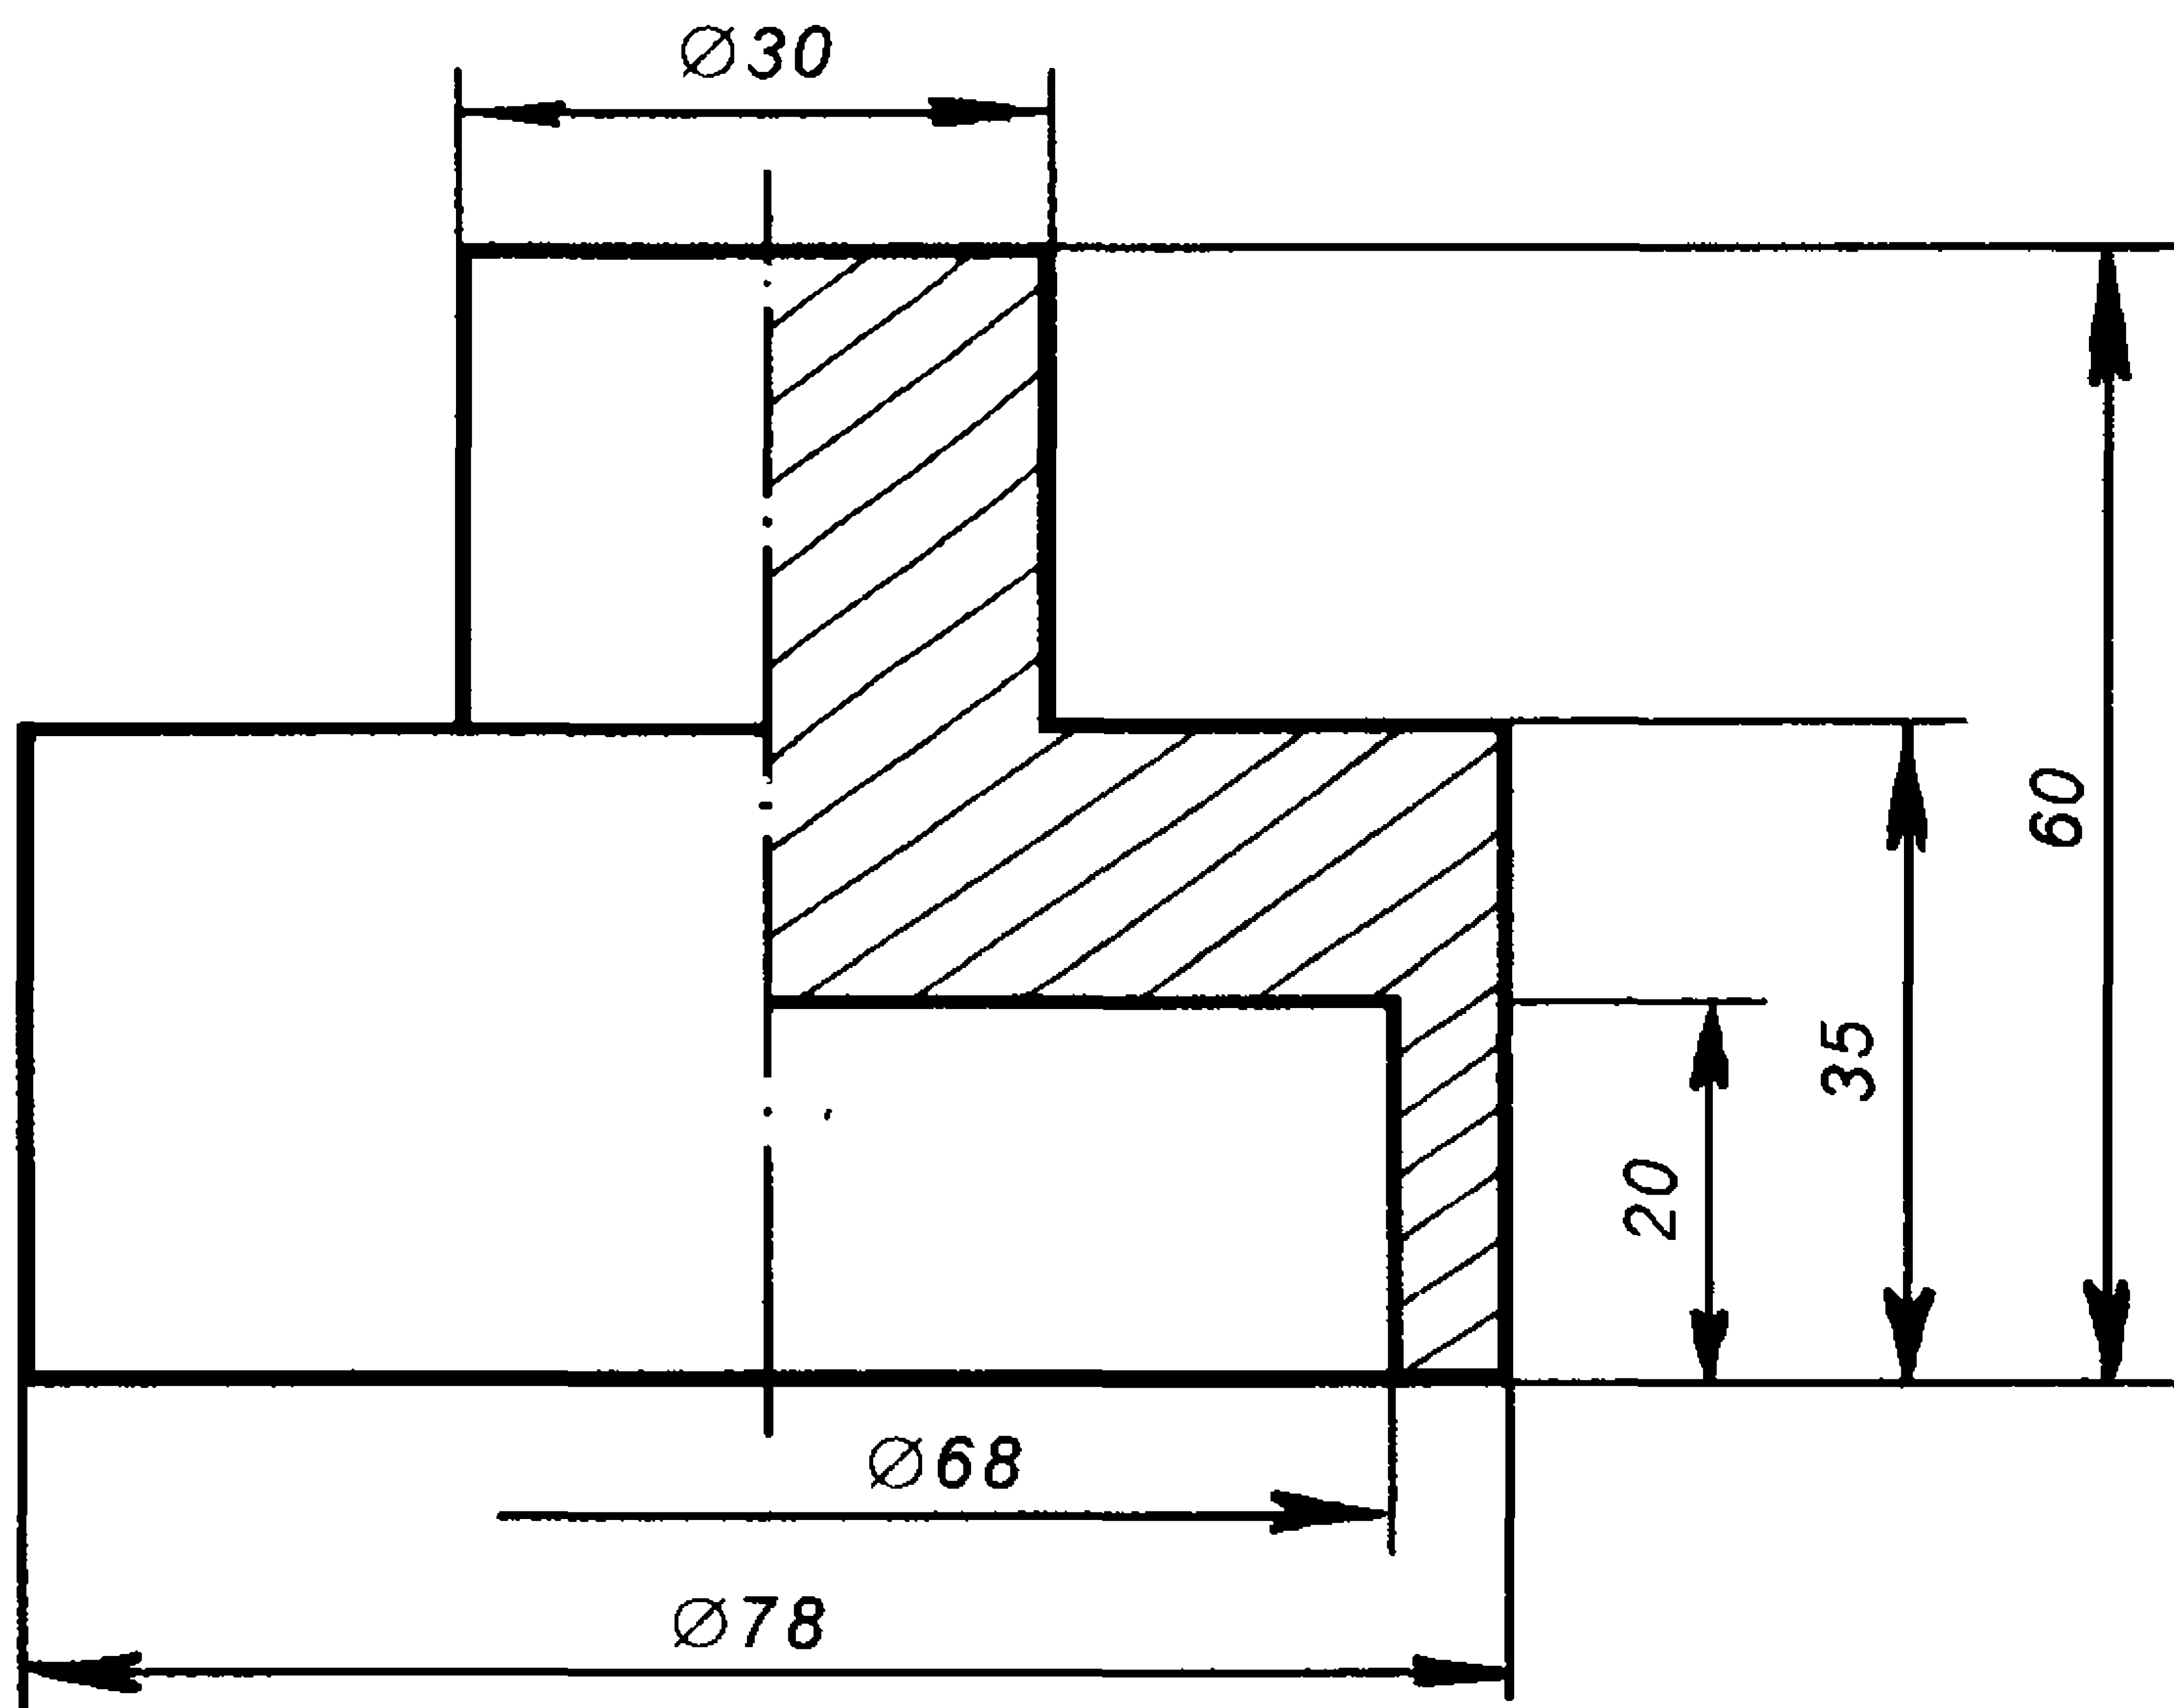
Оправка для запрессовки манжеты в крышку распределительных шестерен
